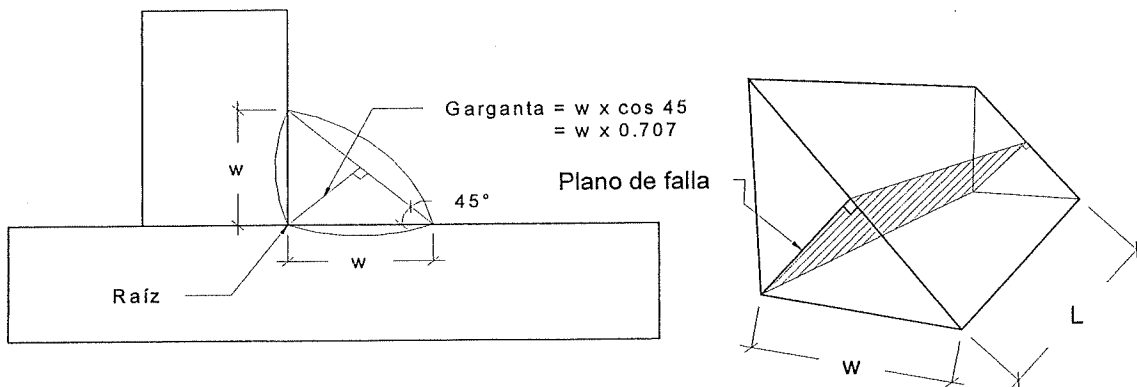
Nomenclatura usada en el diseño de la soldadura.
